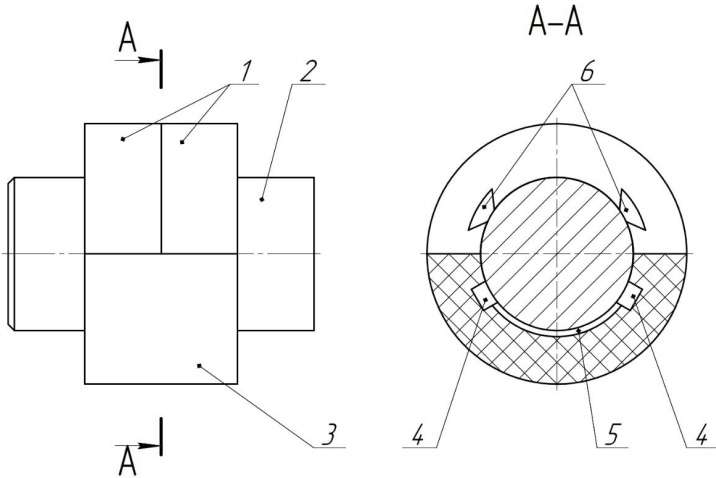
Схема опорного підшипника ковзання, виготовленого з ПКМ
